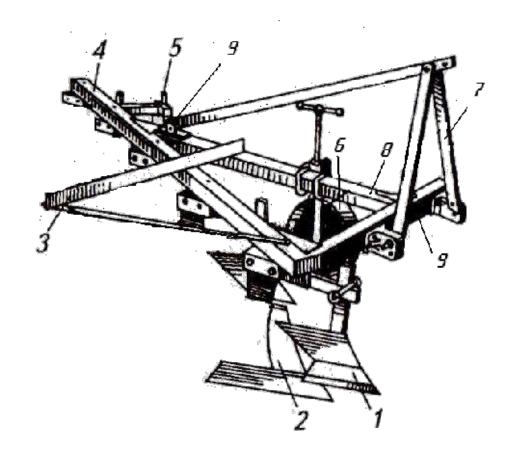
Навесной плуг ПЛН - 5 -35 со снятыми отвалами: 1 – предплужник; 2 – корпус без отвалов; 3 – прицеп для борон; 4 – главная балка; 5 – дисковый нож; 6 – опорное колесо; 7 – навеска; 8 – продольная балка; 9 - поперечная балка.
